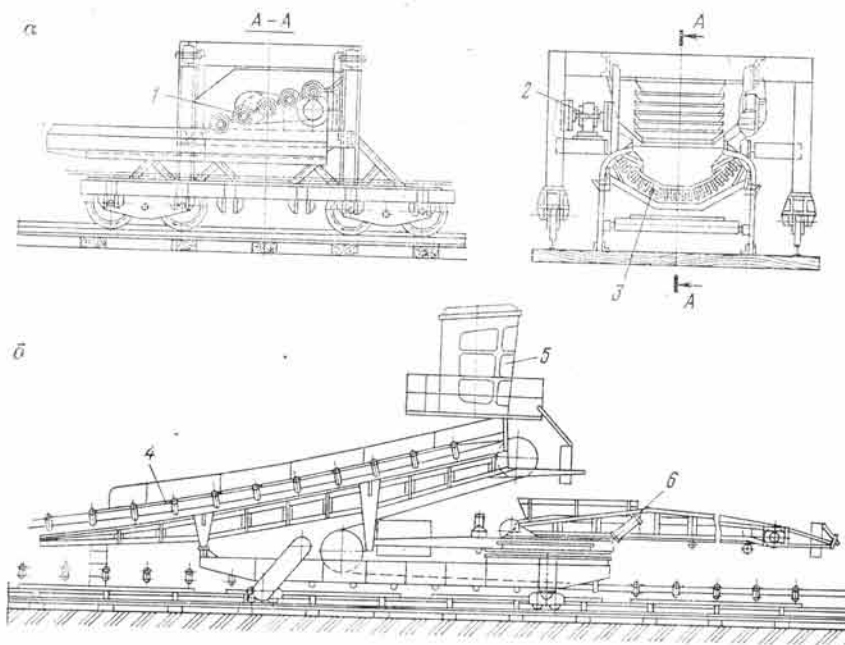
Передвижное загрузочное устройство для забойного конвейера (а) и двухбарабанная разгрузочная тележка (б):
